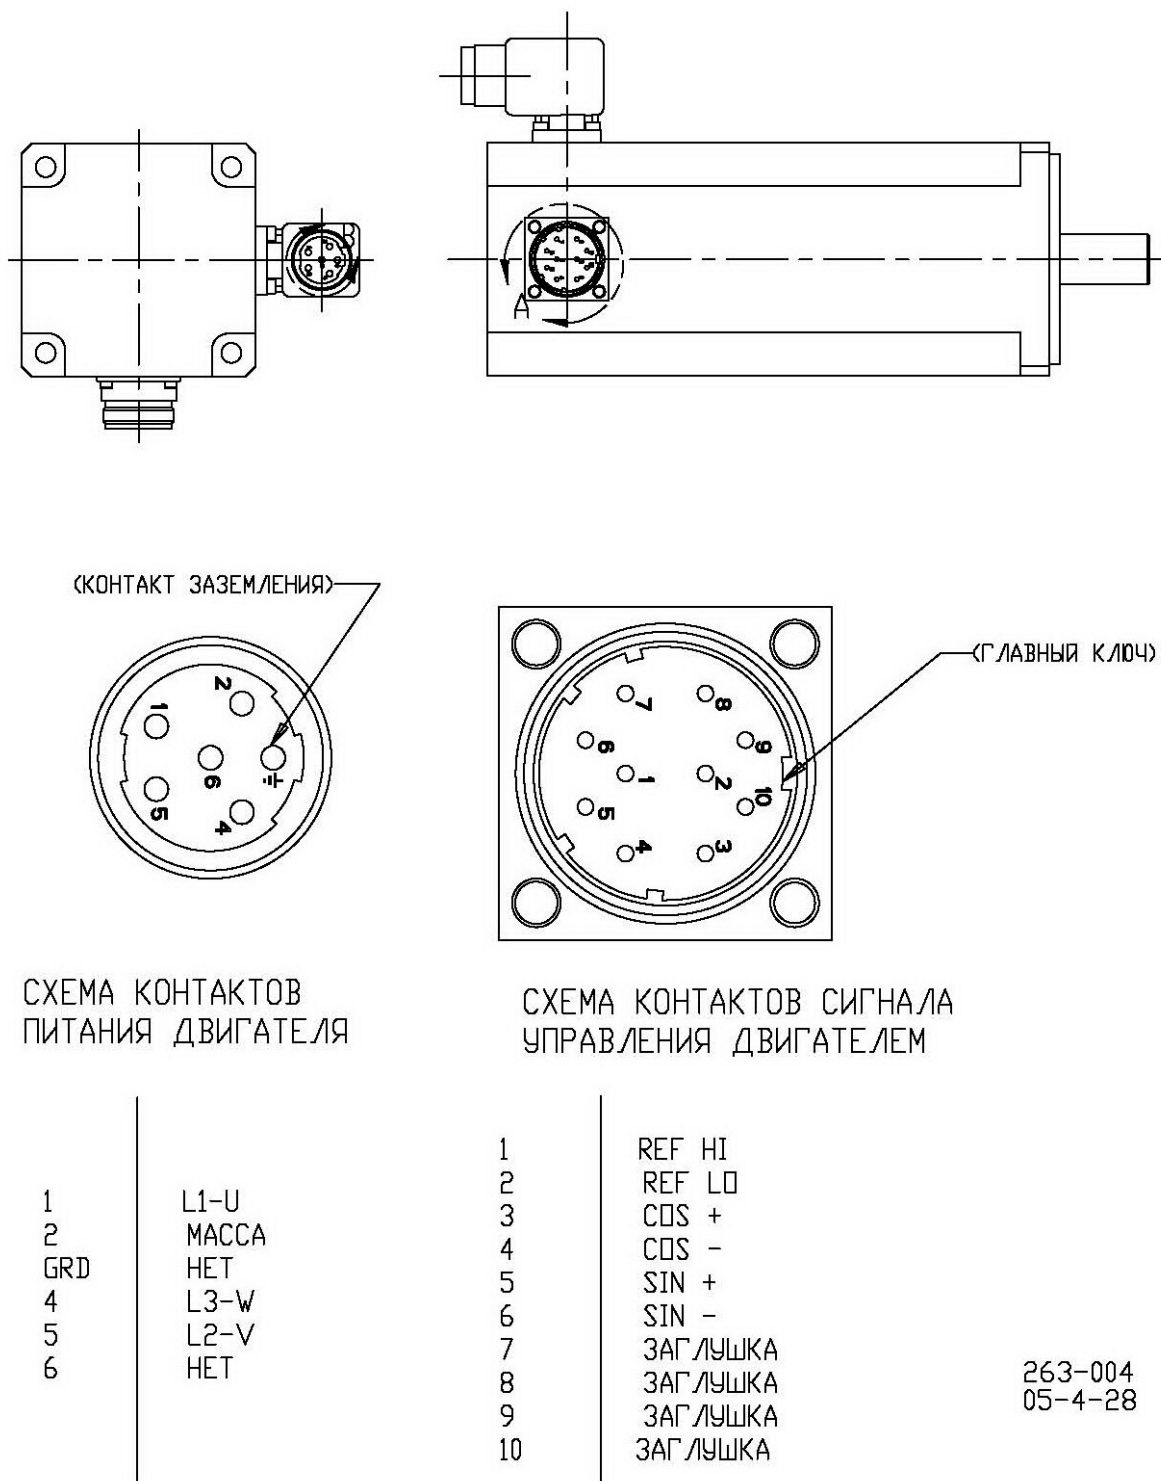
Схема соединений двигателя и преобразователя (для всех клапанов)
